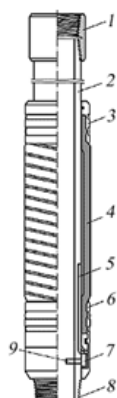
Пакер типа ПЗГ: 1 — муфта обсадной колонны; 2 — корпус; 3 — подвижный обжимной стакан; 4 — уплотнительный элемент; 5 — канал для подвода жидкости; 6 — неподвижный обжимной стакан; 7 — узел клапанный; 8 — резьба обсадных труб; 9 — полый срезной штифт
